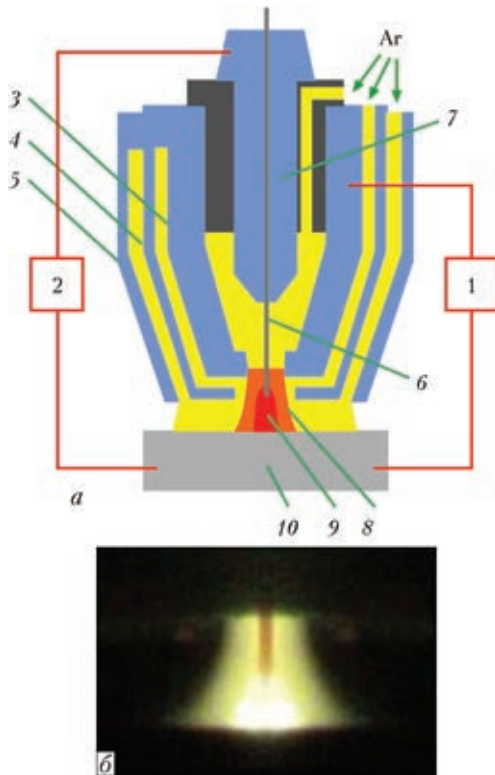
Схема процесса (а) и внешний вид дуги плазменной сварки плавящимся электродом: 1 — источник питания сжатой плазменной дуги; 2 — источник питания МИГ-дуги; 3 — неплавящийся электрод; 4 — стабилизирующее сопло; 5 — защитное сопло; 6 — плавящийся электрод; 7 — токоподвод; 8 — сжатая плазменная дуга; 9 — МИГ-дуга; 10 — изделие
